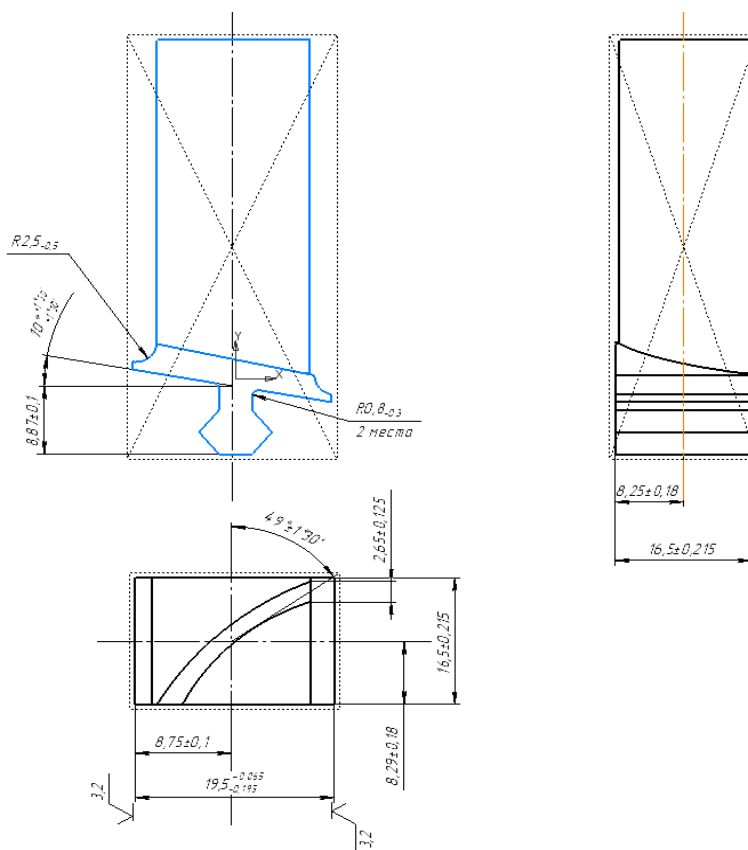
Деталь «Лопатка ротора компрессора высокого давления 5 ступени»
